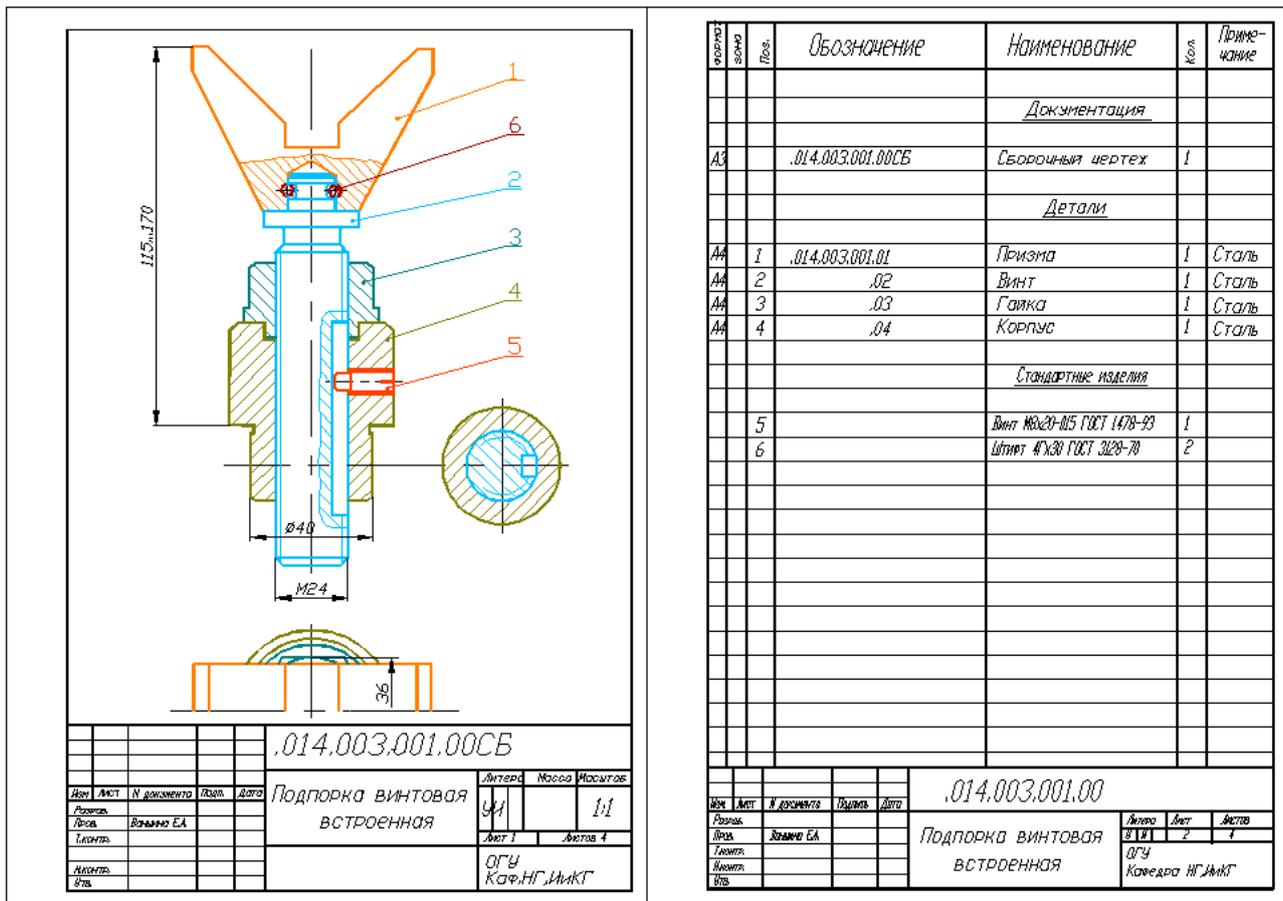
Сборочный чертеж «Подпорка винтовая встроенная».
